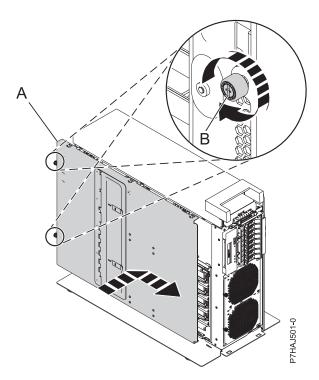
Instalando a Tampa de Acesso de Serviço Interna
